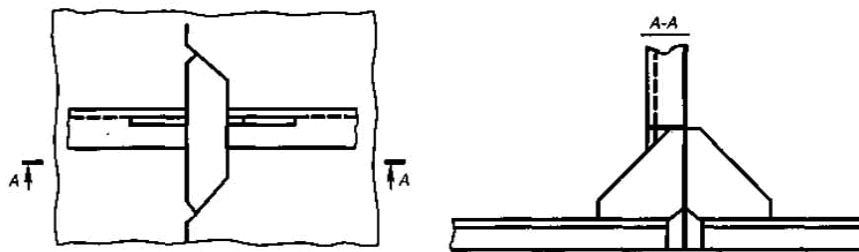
Вузол з'єднання поздовжнього набору з гофрованою перегородкою.
